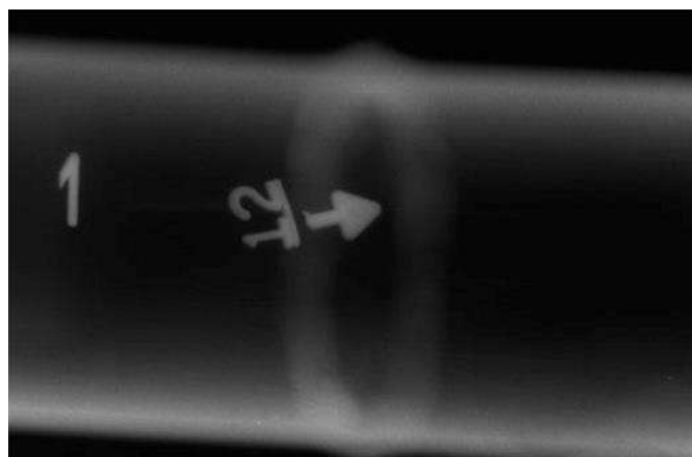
Рентгеновский снимок образца, выполненный за три прохода при сварочном токе 60 А
